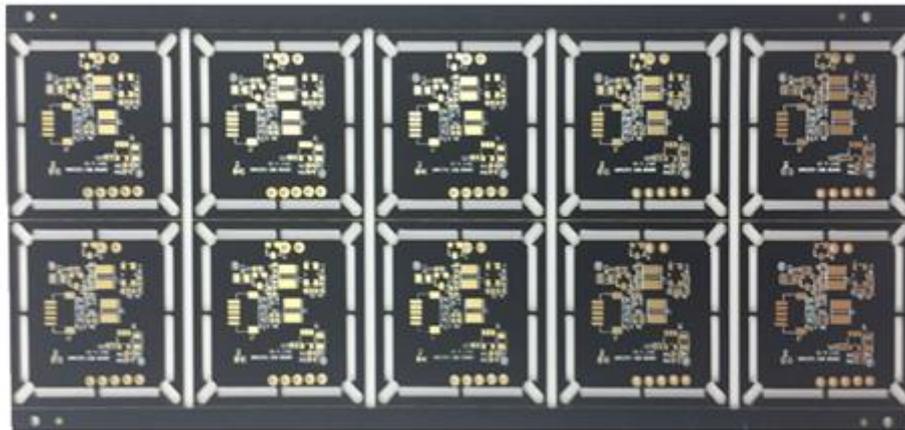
Imagen Ilustrativa de una placa PCB con 10 plaquetas. Nótese que cada plaqueta representa una unidad de producto terminado.
